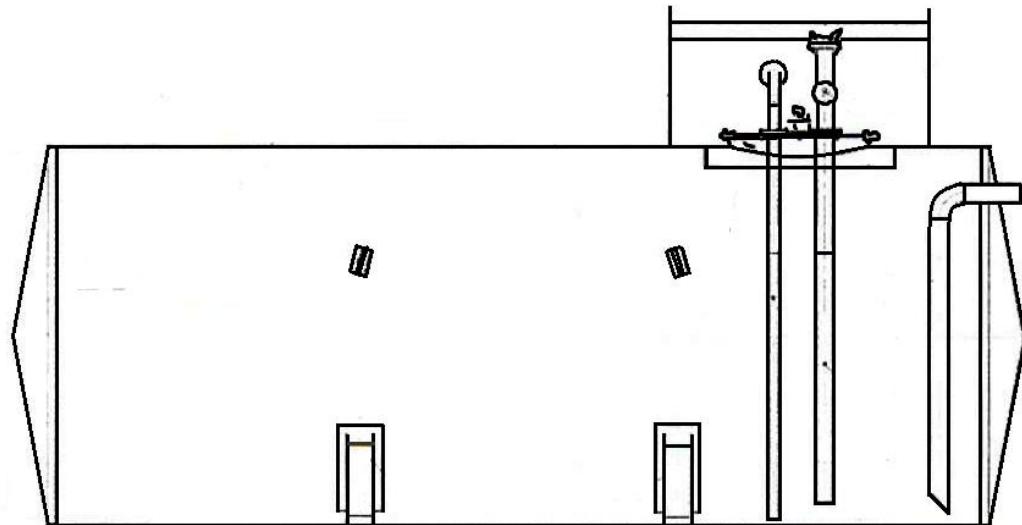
Эскиз резервуаров РГС-20 №№ 635, 636
